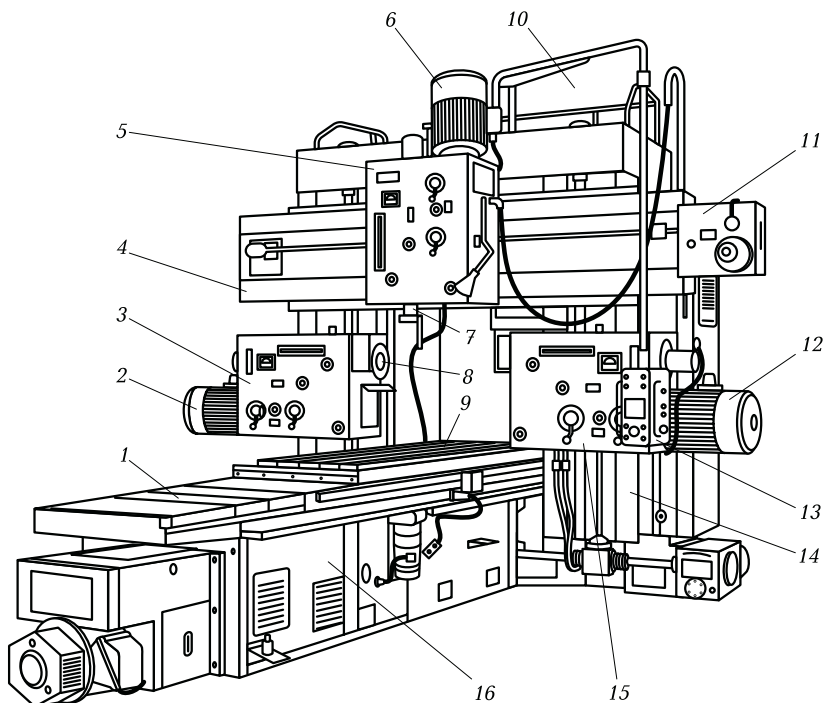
Двухстоечный продольно-фрезерный станок:
